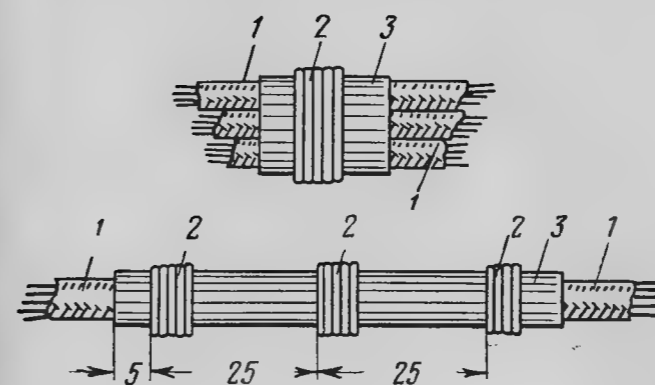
Применение бандажей для заделки разрезной хлорвиниловой трубки, надетой на электропровод (жгут):
